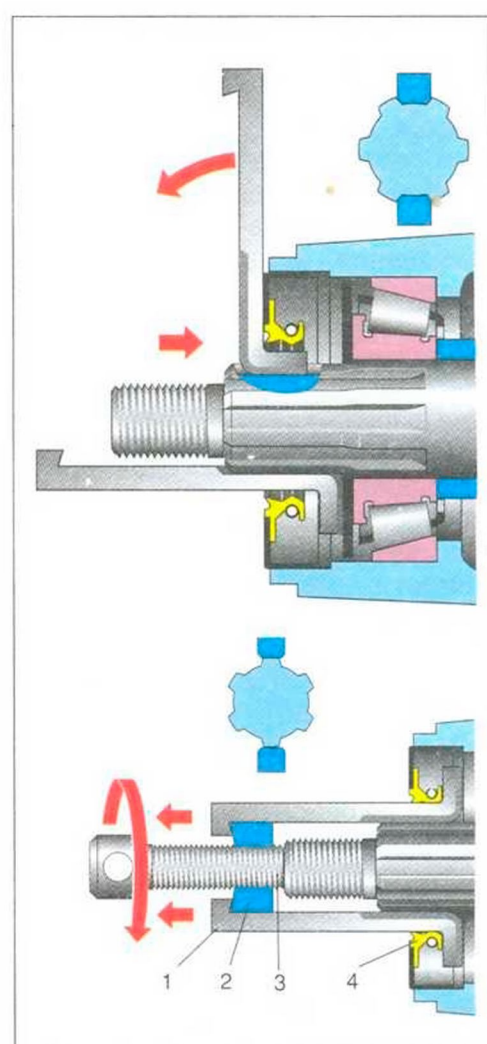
Выпрессовка сальника хвостовика редуктора:
